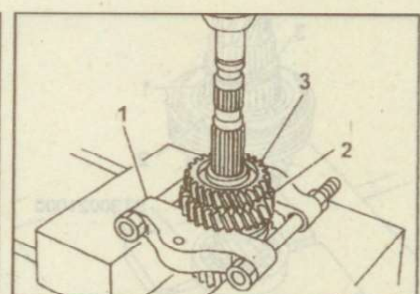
Использование съемника подшипников (1) для снятия шестерни 2-й передачи (2) и шестерни 3-й передачи (3)
